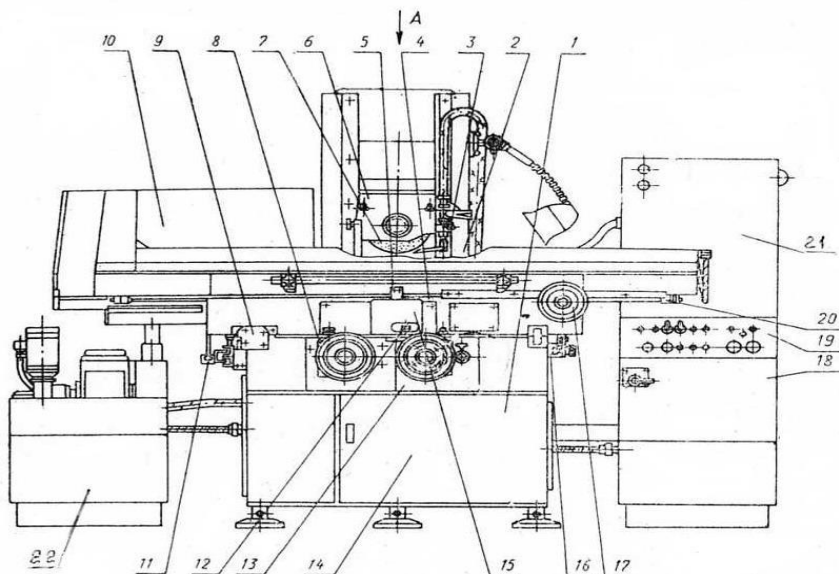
Общий вид плоскошлифовального станка мод. 3E711B
